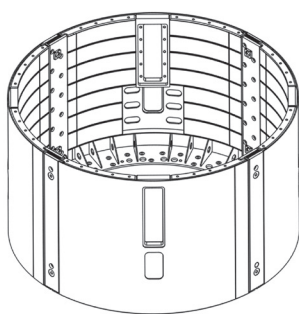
Корпус стабилизирующей секции опытного образца геохода
